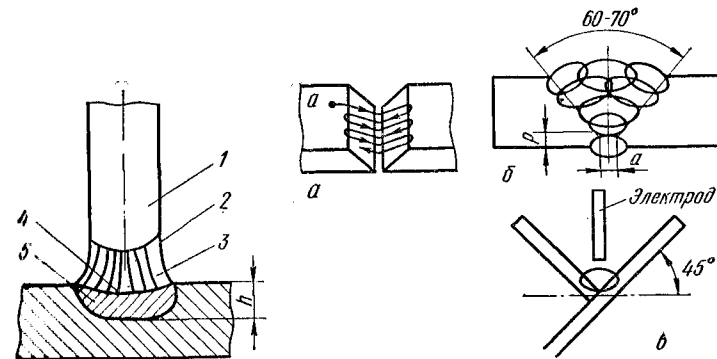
Схема сварочной дуги при сварке металлическим электродом
